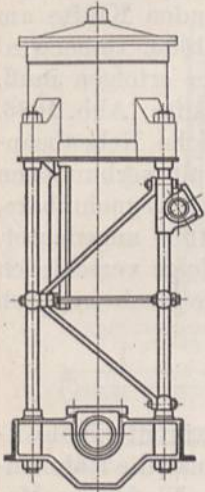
Rahmen für leichte Schiffsmaschinen.
